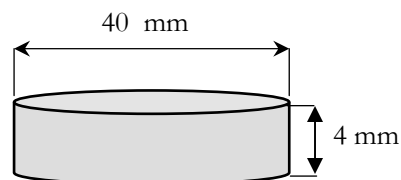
Dimensiones de los discos obtenidos mediante compresión
